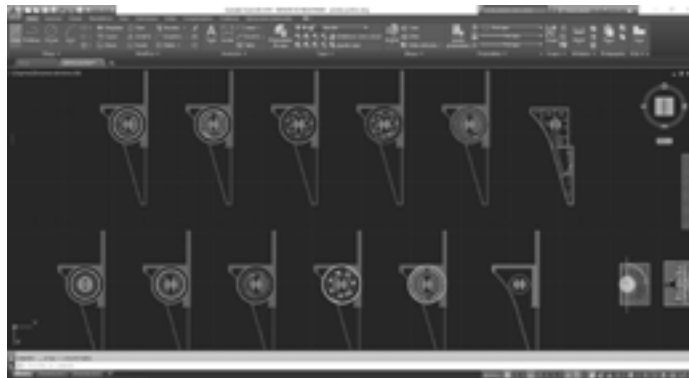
Espacio de trabajo AutoCAD, construcción de la sección. [Fuente: Autor]
